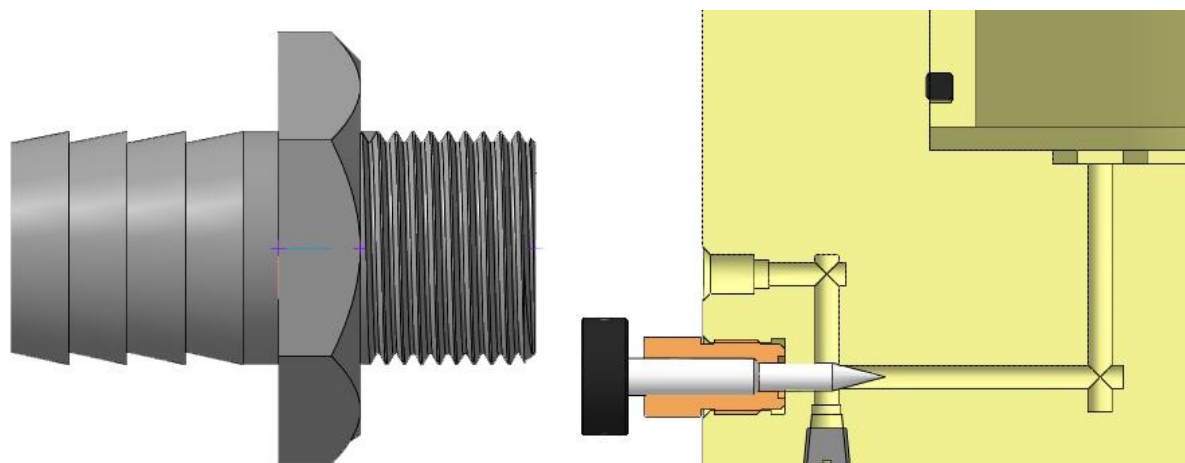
Цилиндрический штуцер и цилиндрическое отверстие в корпусе капилляриметра
